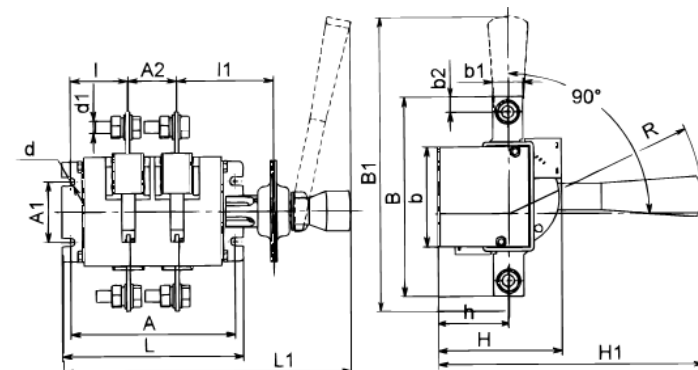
Б Выключатель-разъединитель на одно направление двухполюсный с боковой смещенной рукояткой
